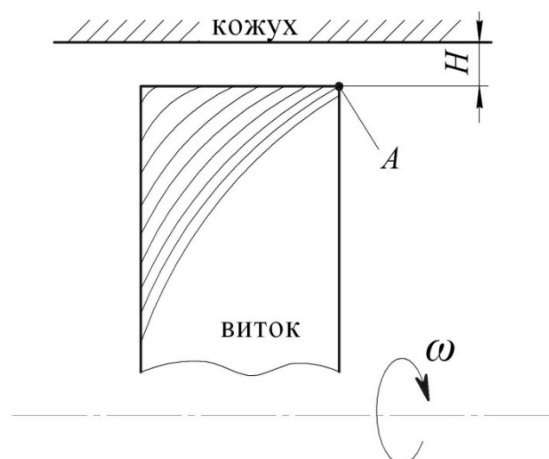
Схема профілів зношування периферійної частини витка шнека
